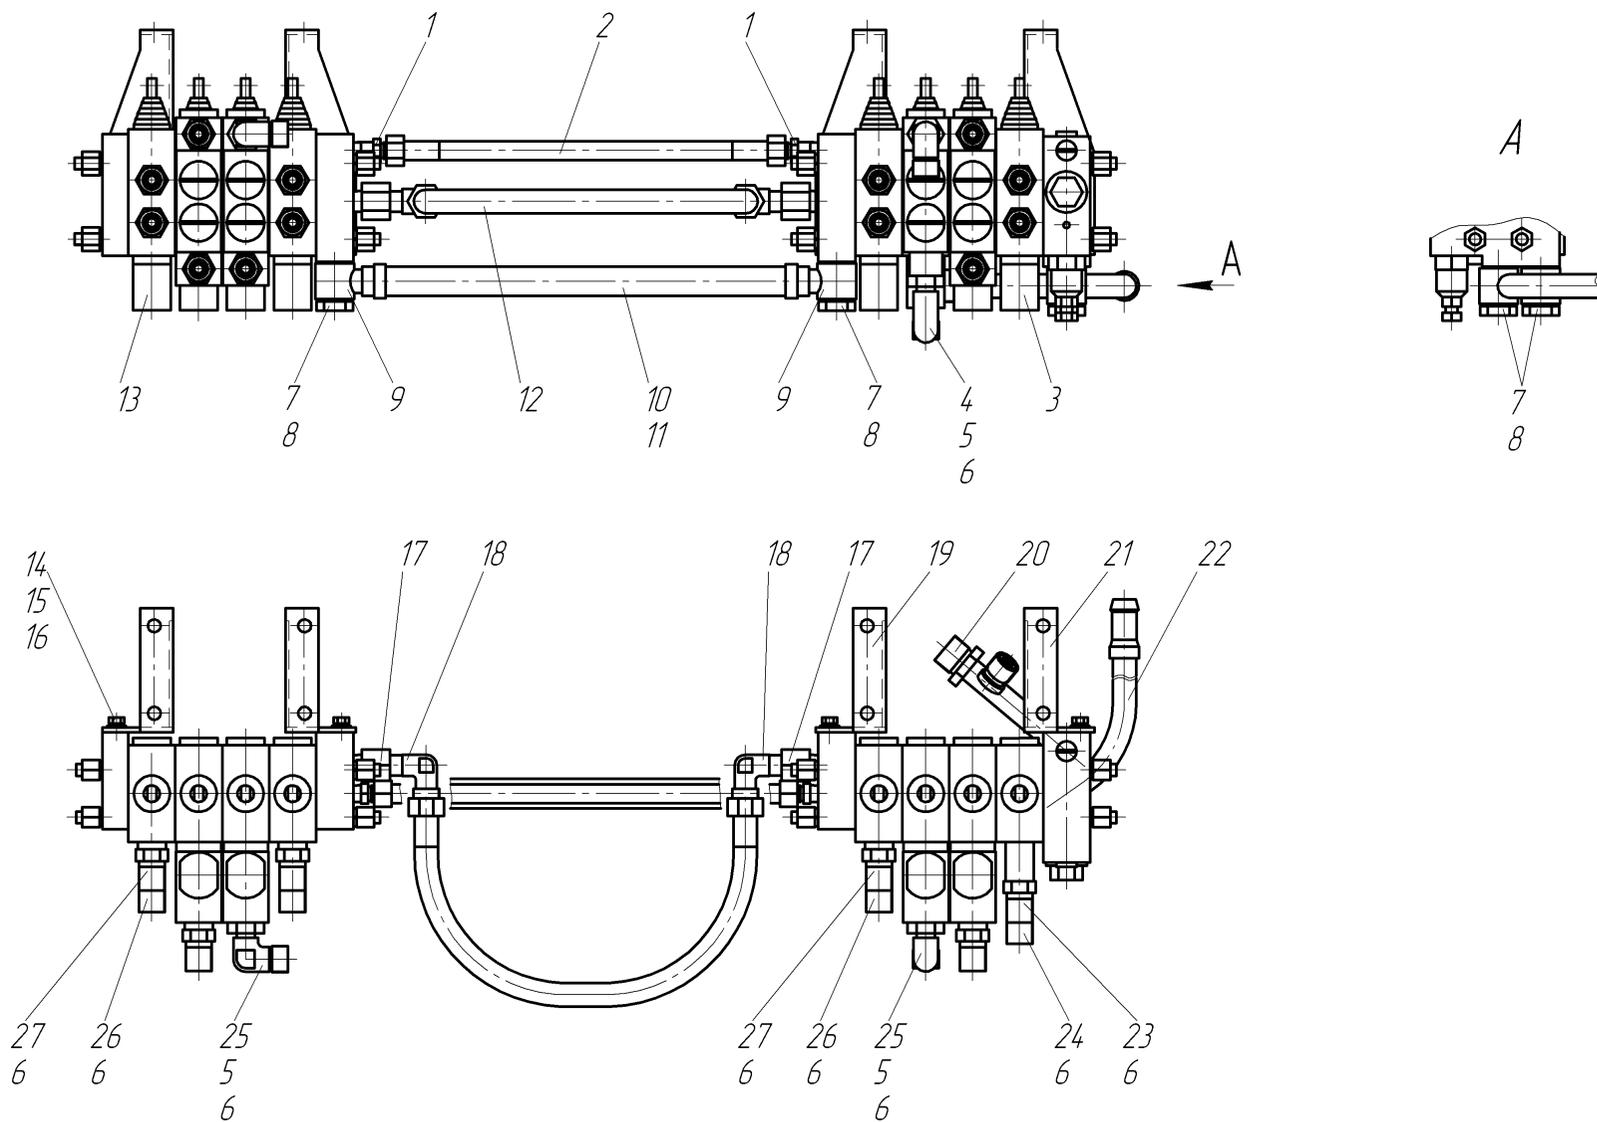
Установка гидрораспределителя 273.05.02.00.000
